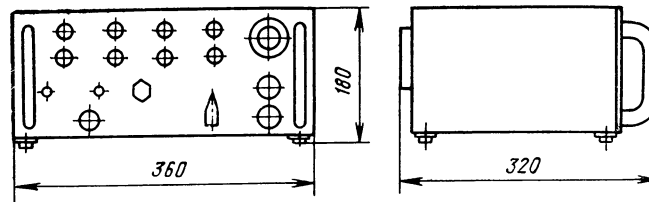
Габаритные и присоединительные размеры блока управления, розжига и сигнализации БУРС-1
